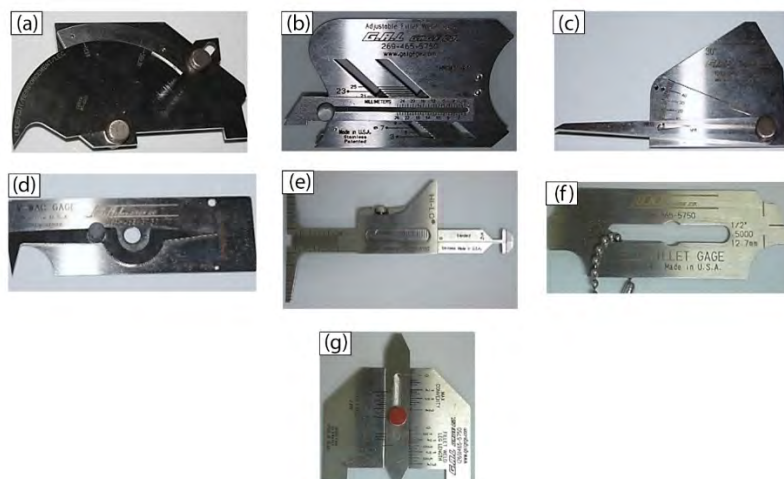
(a) Cambridge Gauge, (b) Adjustable Fillet Weld Gauge, (c) Weld Size Gauge, (d) Hi-Lo Gauge, (e) Skew - T Fillet Gauge, (f) Fillet Gauge, y (g) V - WAC Gauge
